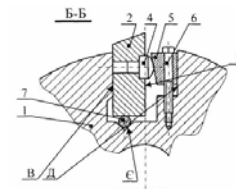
Узел крепления режущего элемента червячной фрезы для обработки крупногабаритных зубчатых колес
